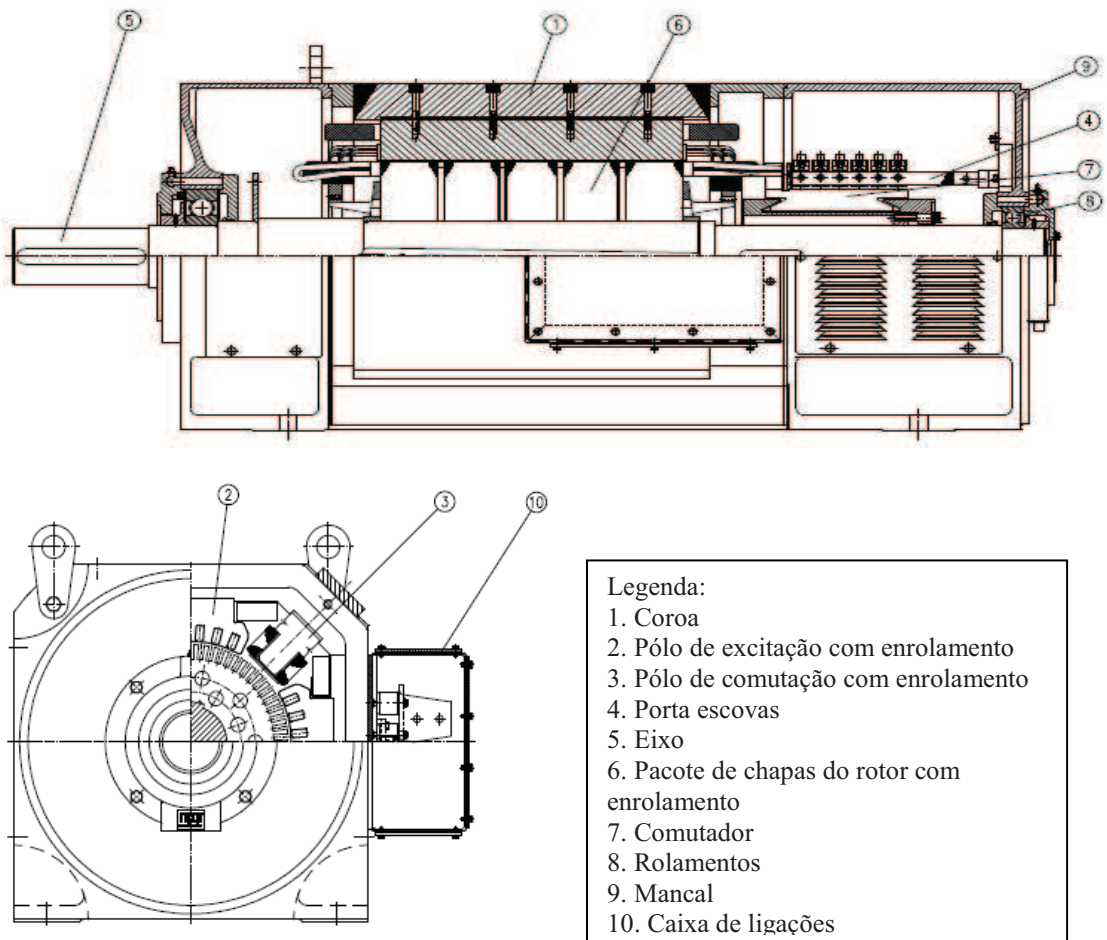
Partes Principais do Motor de Corrente Contínua [46]
